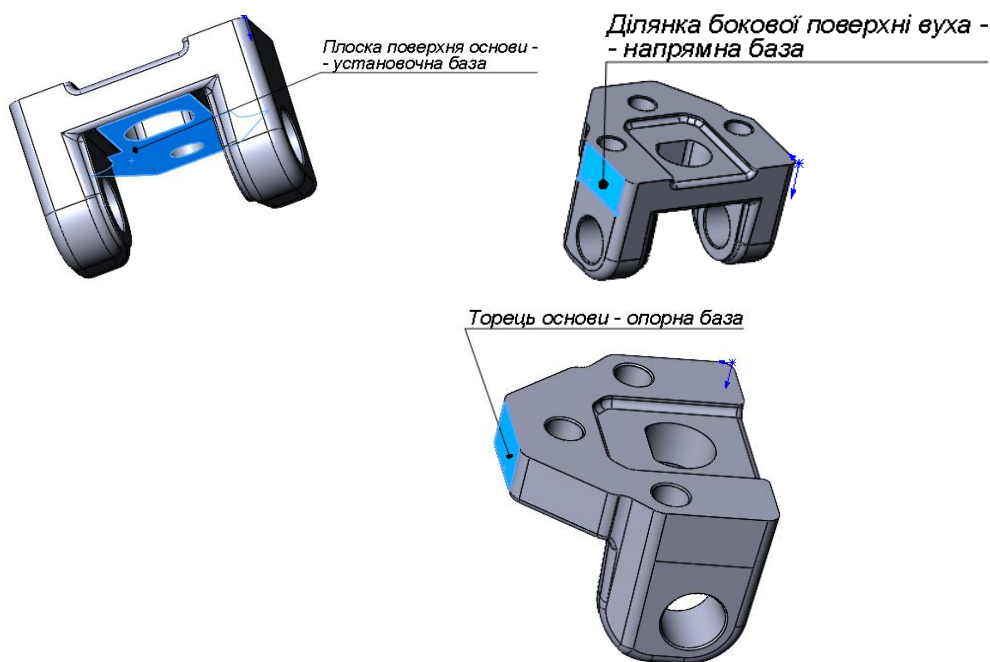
Вибір поверхонь заготовки для її базування.
